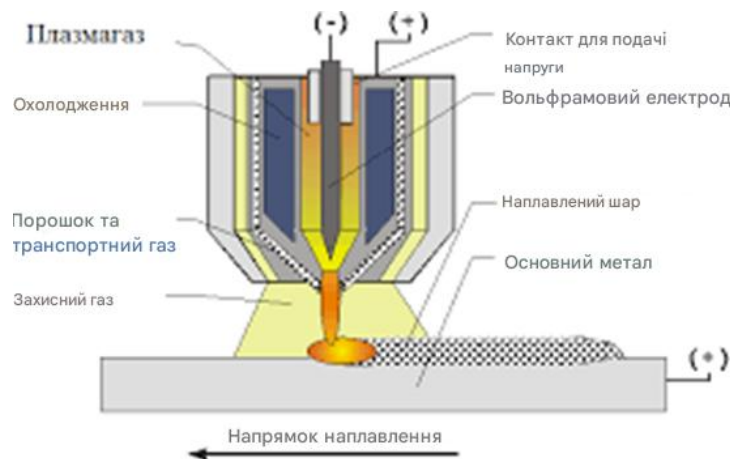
Схема процесу плазмового наплавлення деталей
